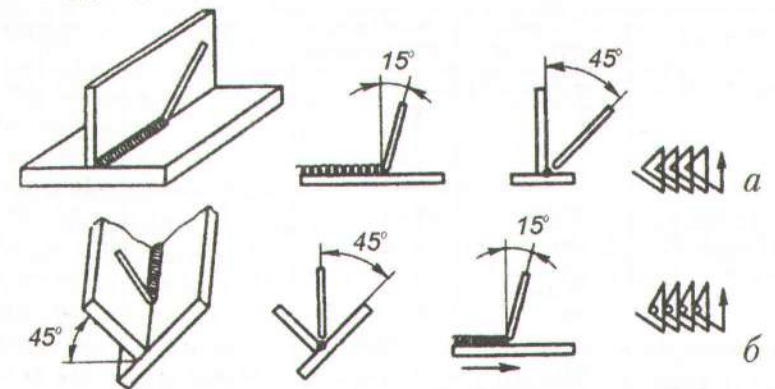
Зварювання кутових швів із коливальними рухами електрода: а — трикутником без затримки в корені шва; б — трикутником із затримкою в корені шва
